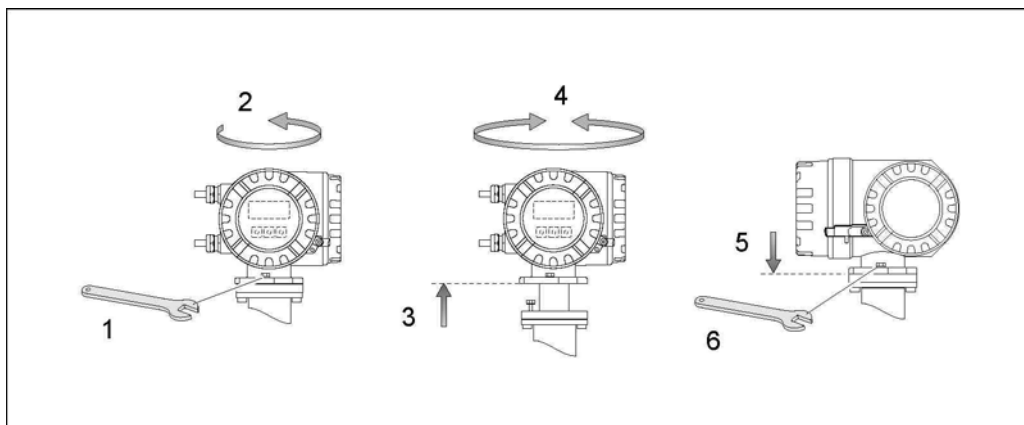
Вращение корпуса преобразователя (алюминиевый полевой корпус)
